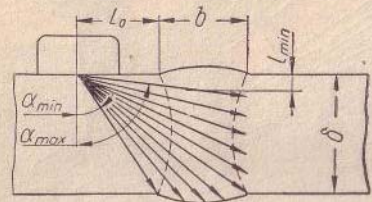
Схема прозвучивания сварных швов при контроле методом качающегося луча.
